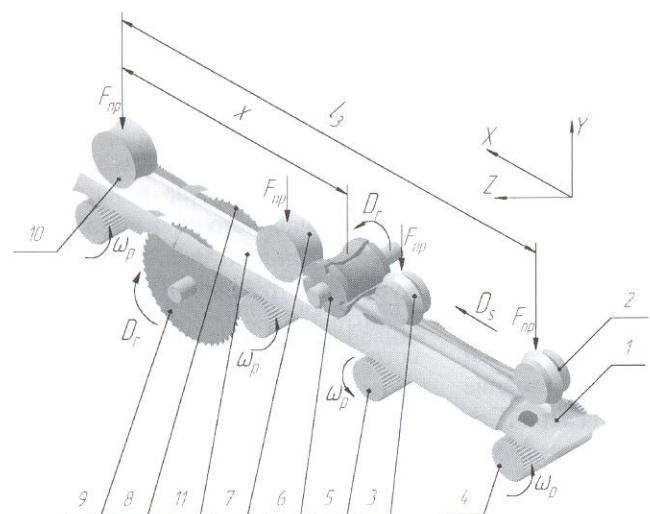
Схема обработки горбыля на станке ПФП-100 с направлением заготовки роликами специального профиля
